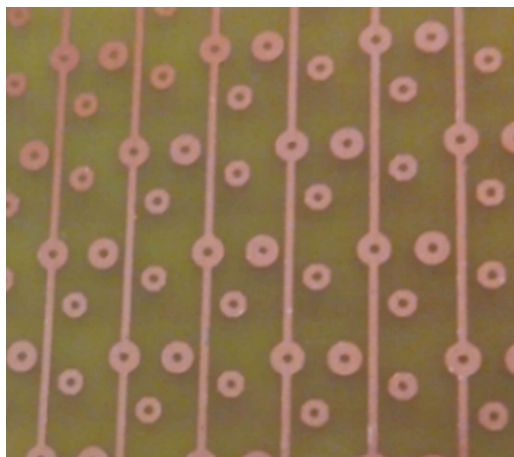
PCB después del atacado. 35 μm , 100 s
